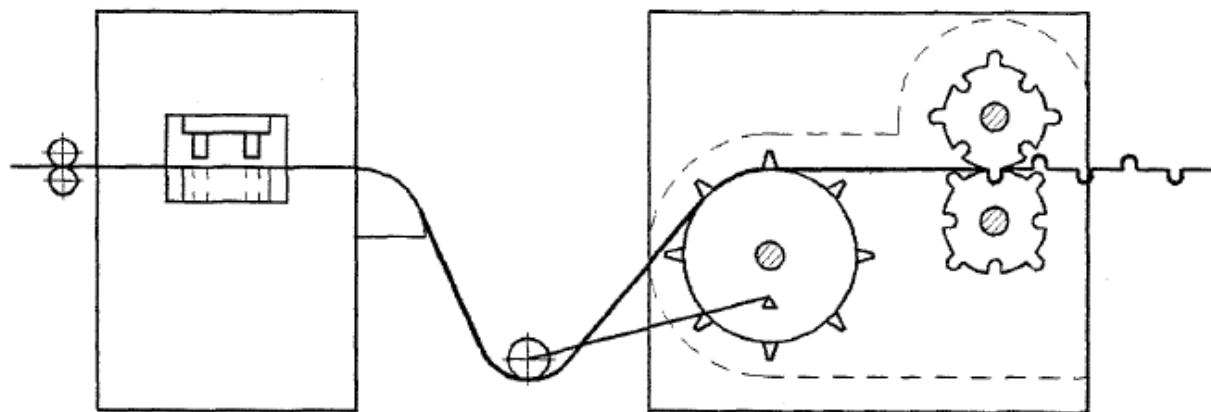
Установка для изготовления ленты с отверстиями в вершинах гофров
